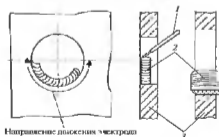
Схемы обварки отверстия в целях уменьшения размеров: 1 — электрод, 2 — изделие, 3 — шов
